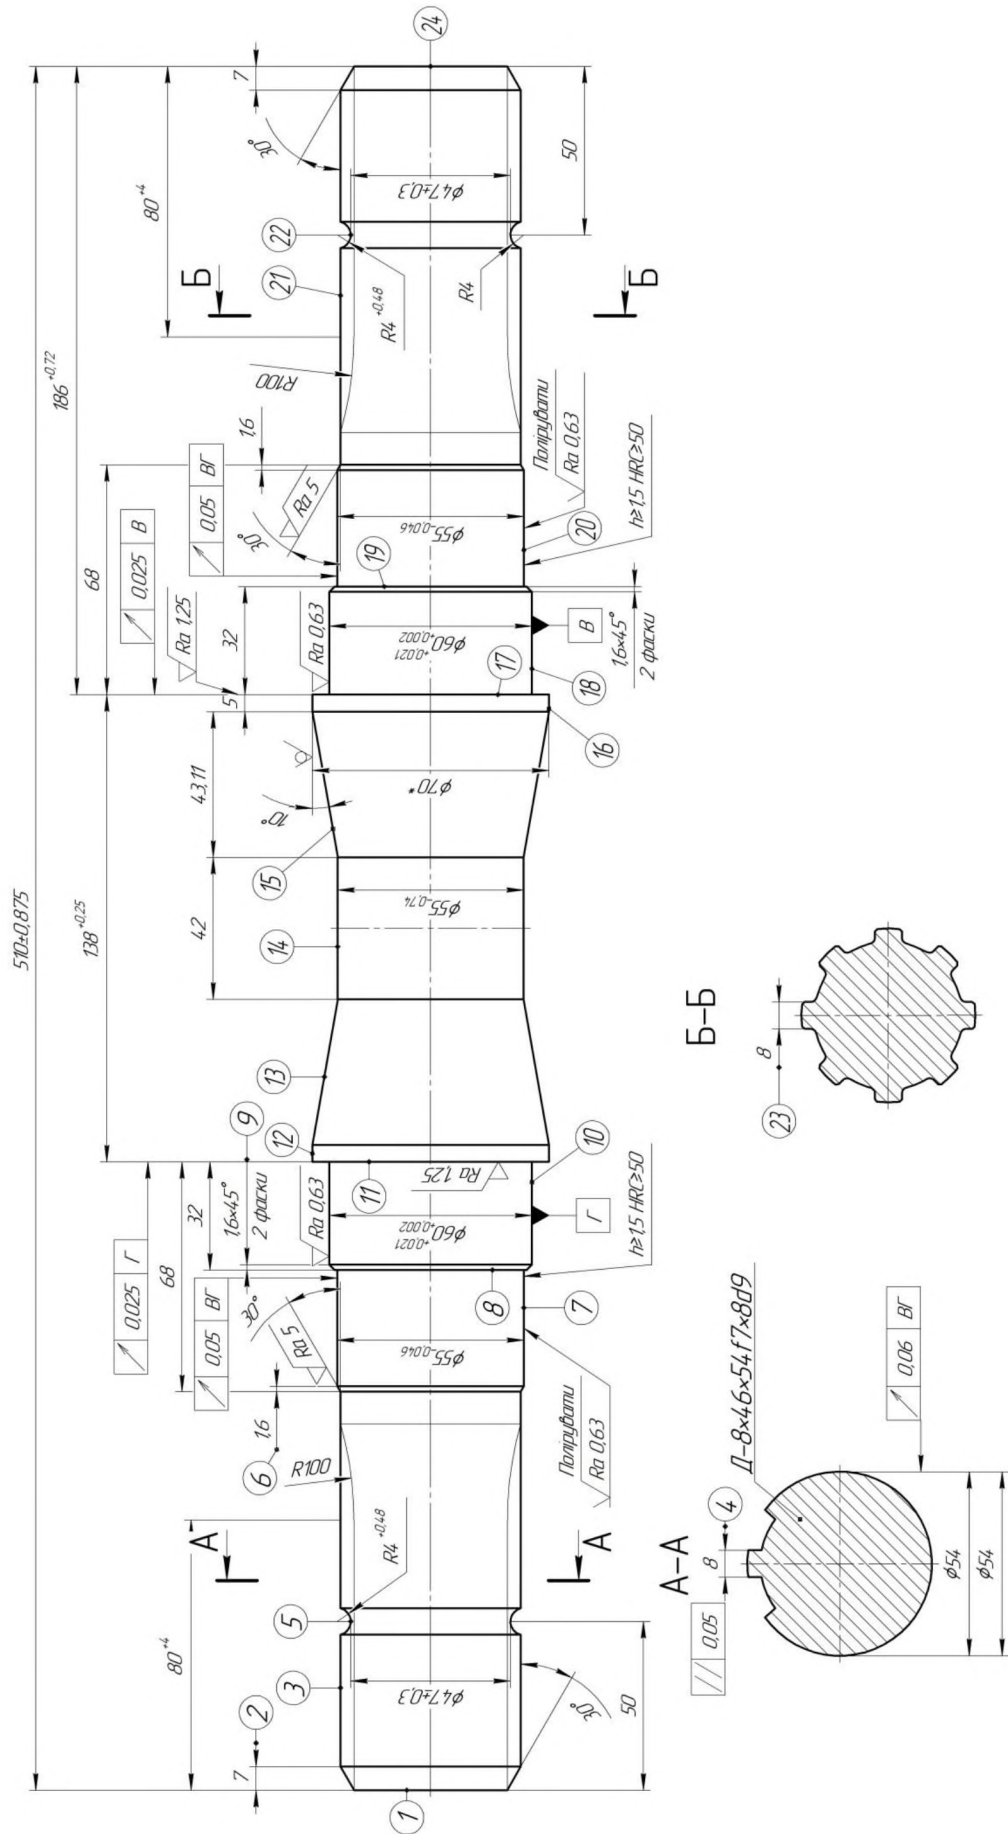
Нумерація поверхонь деталі «Вал шліцьовий»
